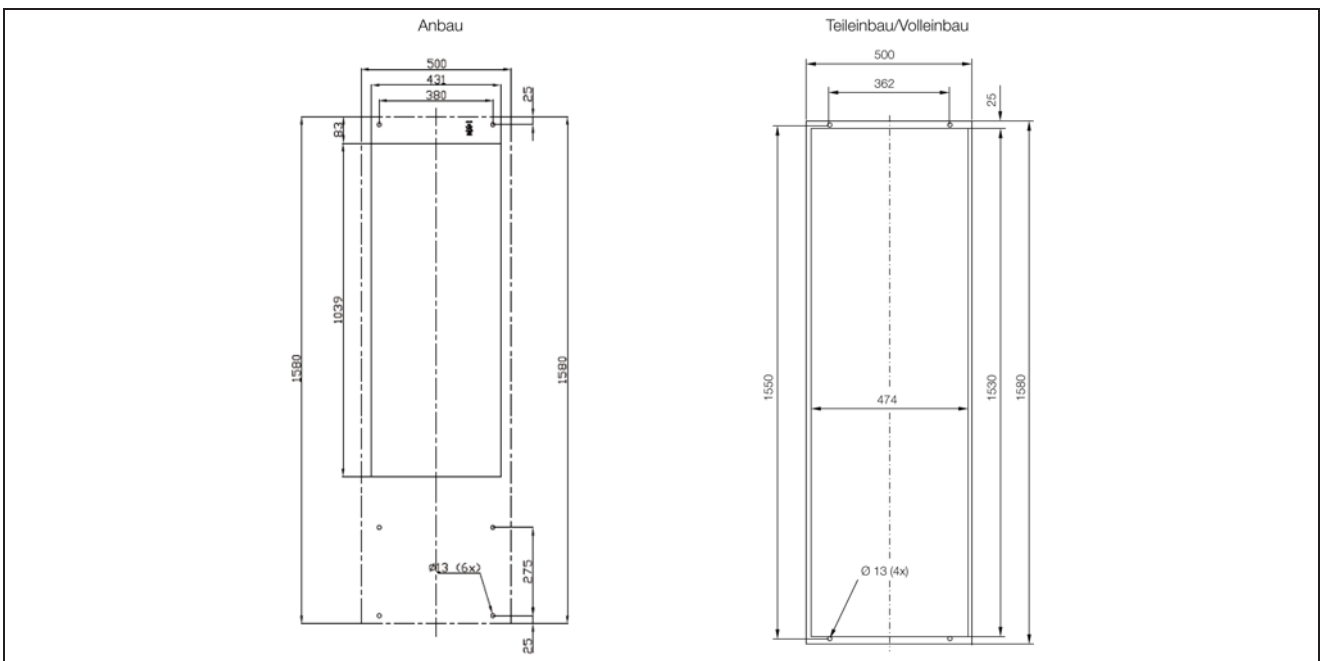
Montageausschnitt für Anbau/Teileinbau/Volleinbau
